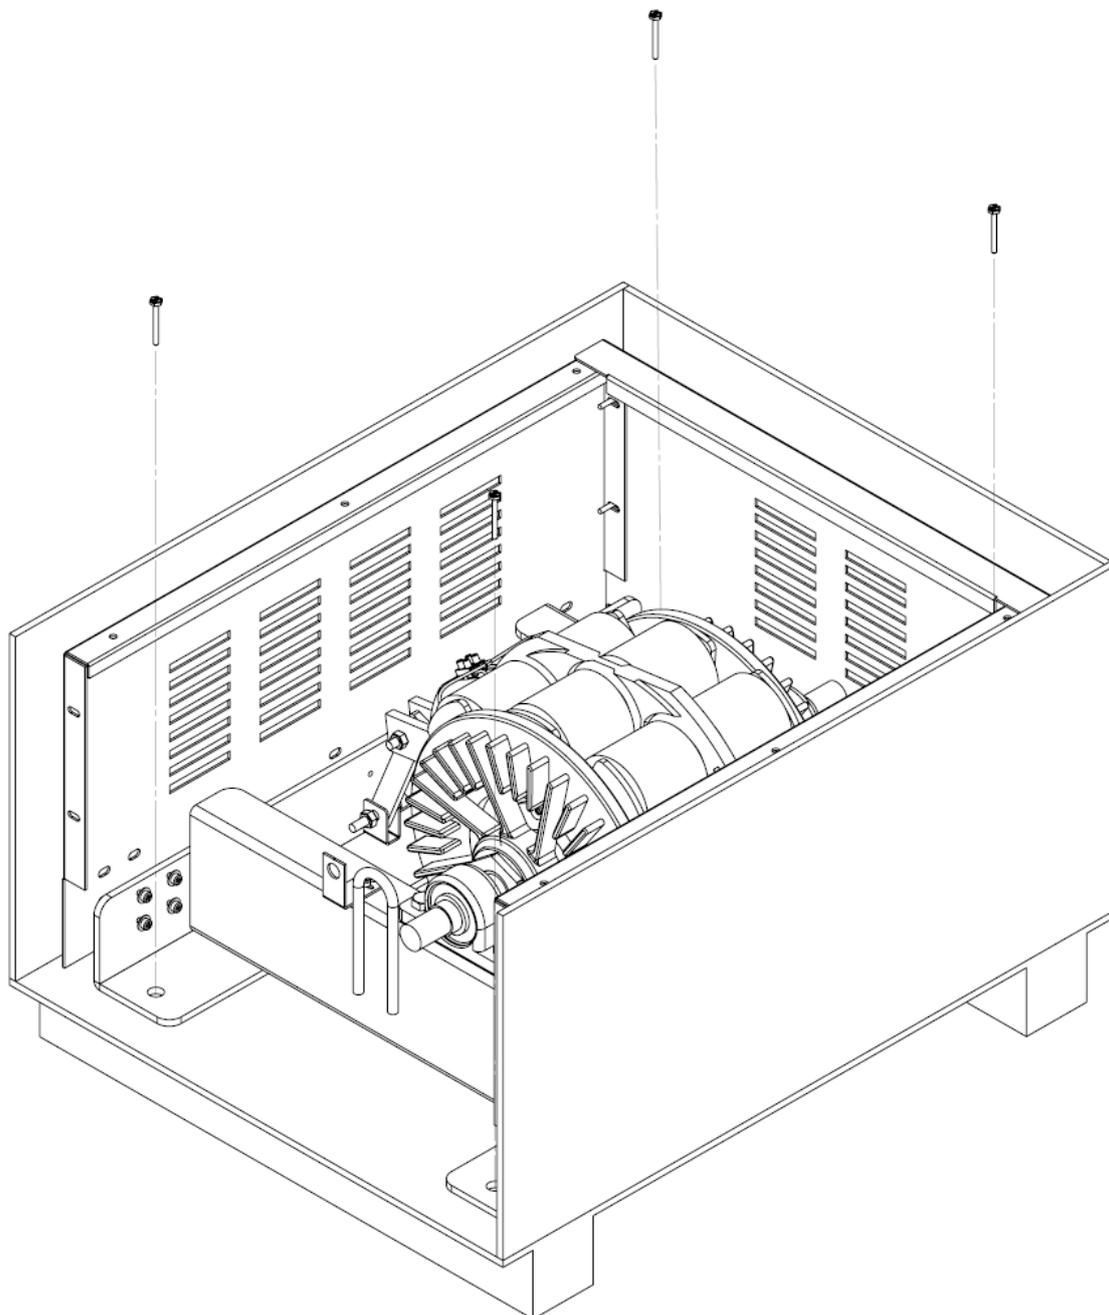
Remoção dos parafusos de fixação da caixa de embalagem
